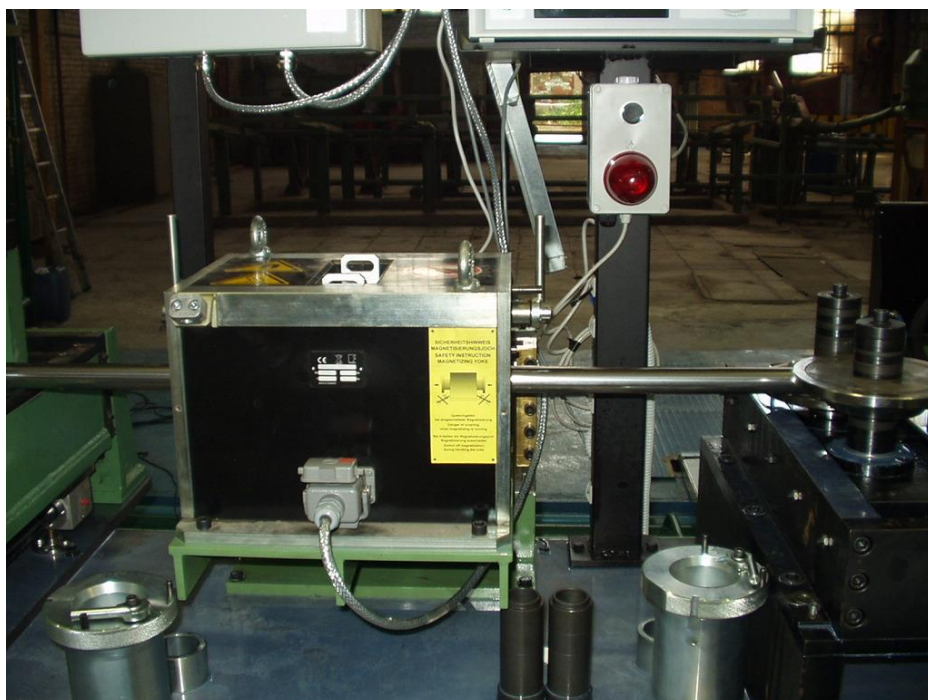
Проходной вихретоковый преобразователь для контроля сварных труб из нержавеющей стали.
